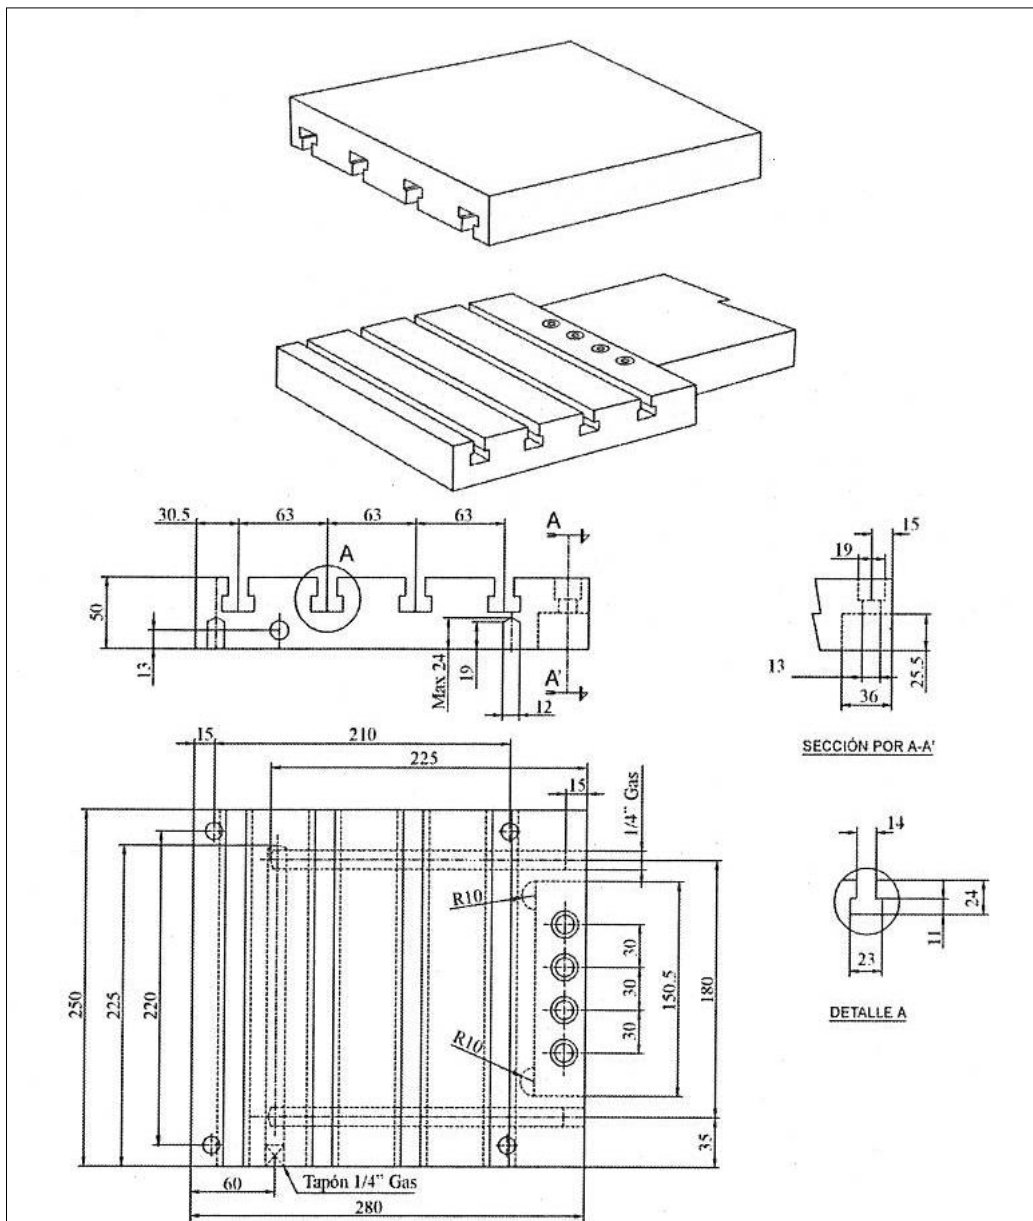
Detalle constructivo de las mesas (inferior y superior) de una prensa apta para la soldadura por proyección.
